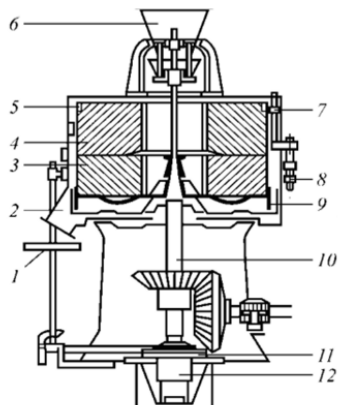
Схема жернового поста: 1 - установочный маховик; 2 - выводной штуцер; 3 - нижний жернов; 4 - верхний жернов; 5 - бандаж; 6 - питающая воронка; 7 – кожух; 8 - нажимные пружины; 9 - опорно-приводное колесо; 10 - центральный вал с приводом; 11- червячная пара; 12 – подпятник.
